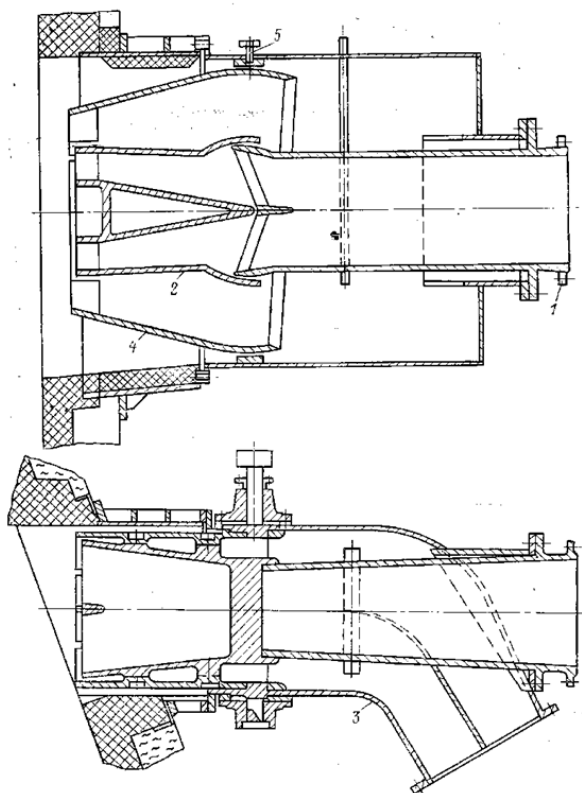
Поворотная горелка ЗИО (1 – фланец пылепровода; 2 – сопло первичного воздуха; 3 – короб вторичного воздуха; 4 – сопло вторичного воздуха)
